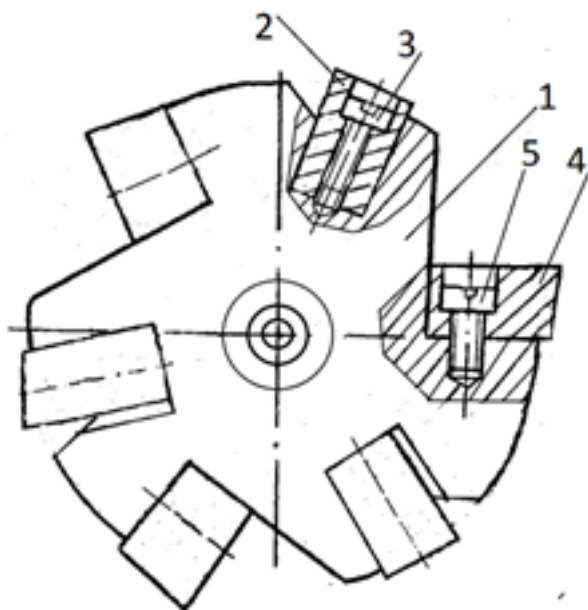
Вид торцово-цилиндрической фрезы со стороны торцовой части, имеющей торцовые пластины с радиальным креплением, а дополнительные торцовые пластины с тангенциальным креплением
